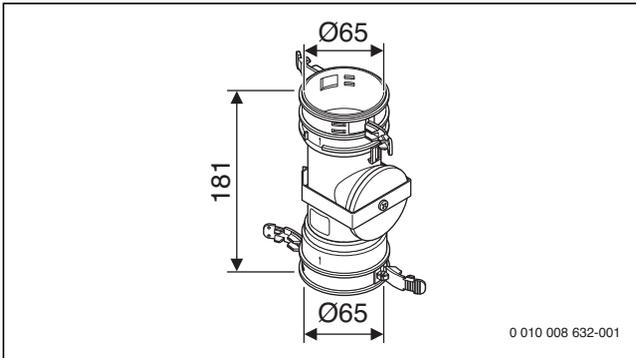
Verbindungsstück Flex mit Prüföffnung Ø 60 mm (Maße in mm)
